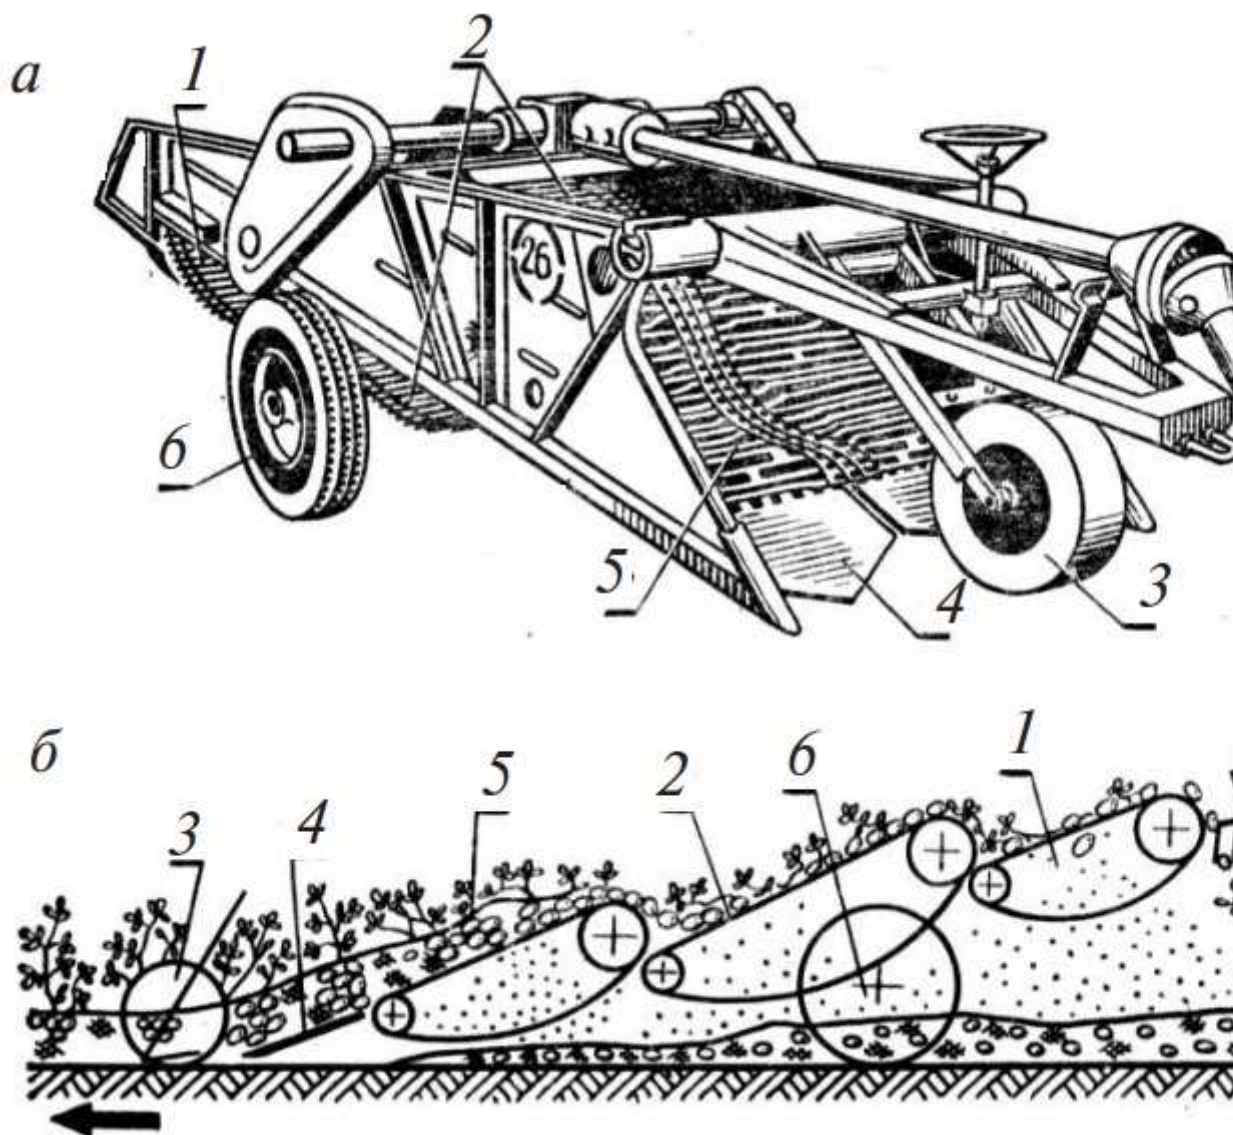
Картофелекопатель КСТ-1,4: а - устройство; б - схема работы; 1 - каскадный элеватор; 2 - основной элеватор; 3 - опорный каток; 4 - лемех; 5 - скоростной элеватор; 6 - ходовое колесо; 7 - сужающий щиток
